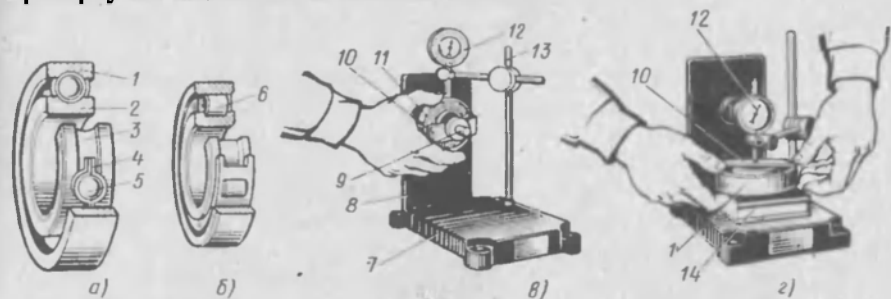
Устройство однорядного шарикового (а), роликового (б) подшипников качения и приспособлений для проверки в подшипниках радиального (в) и аксиального (г) зазоров:
